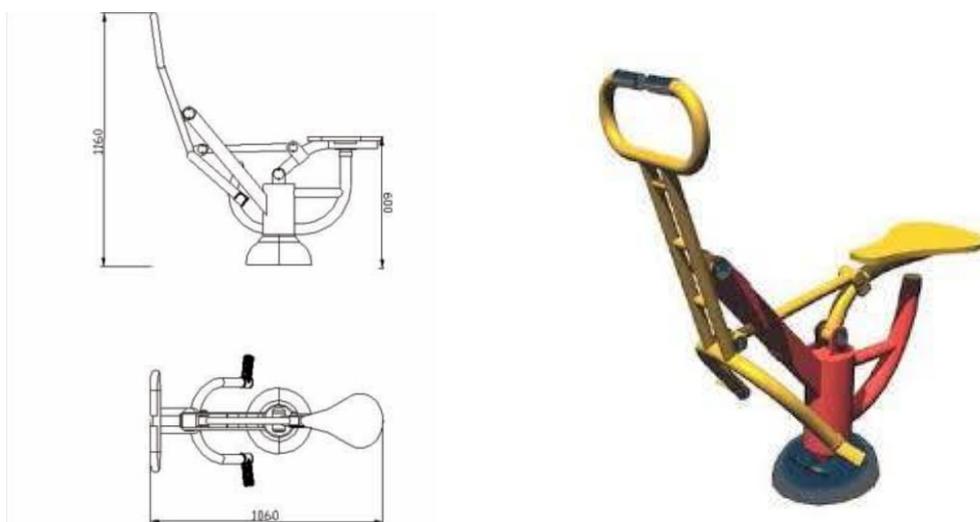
Alzado, perfil y representación 3D poni
